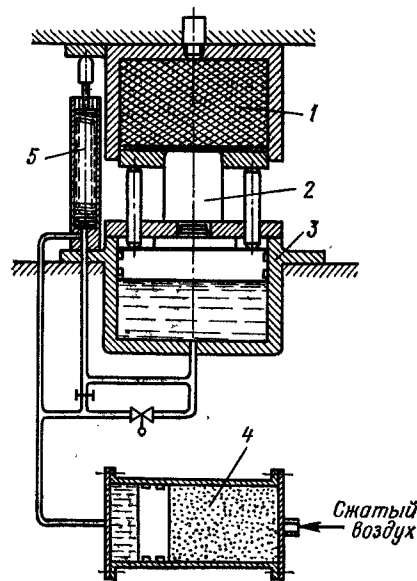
Схема установки для вытяжки резиновой матрицей;
